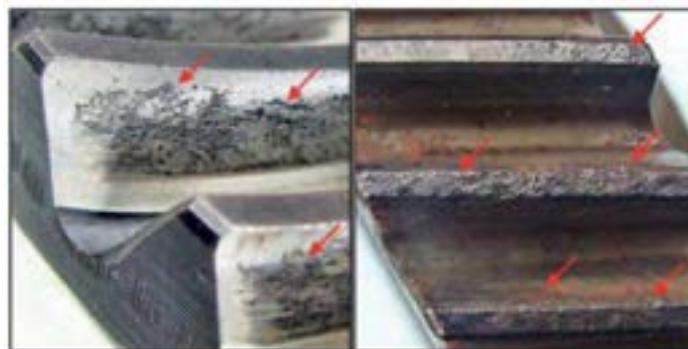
Corrosión sobre dientes de engranajes
